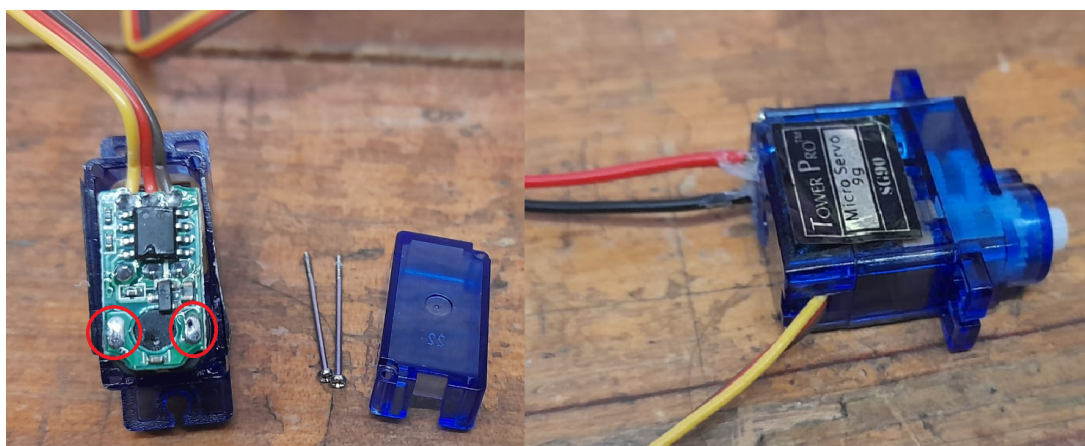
Adaptação elétrica do motor: soldagem direta nos terminais.
